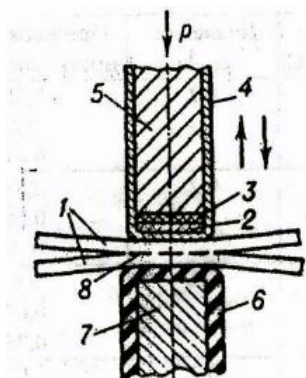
Схема термоимпульсной сварки пленок:
